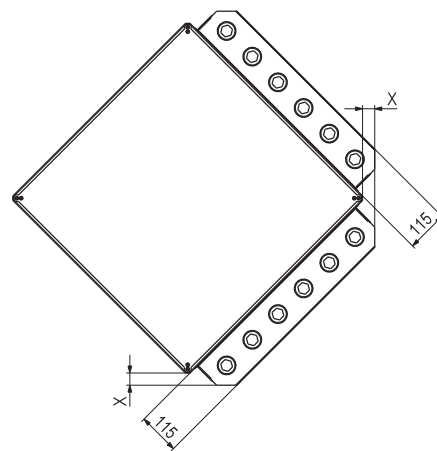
Maßblatt für Krivan Plattenwärmetauscher mit Klappen (Maße in mm)
